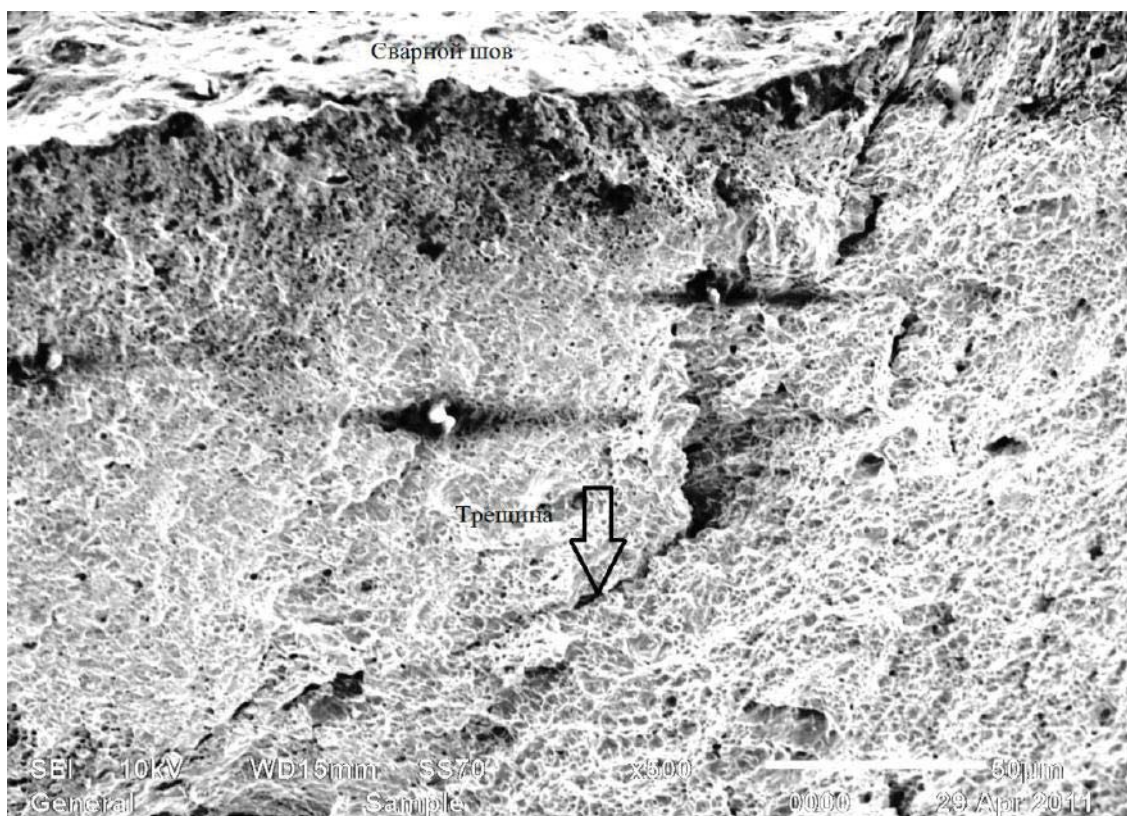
Околошовная зона сварного соединения стали 30ХГСА
